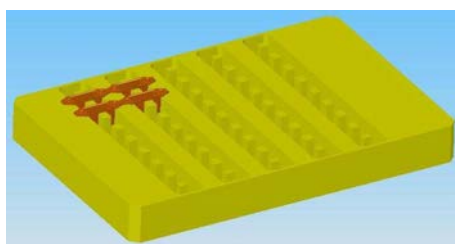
Support à cuvettes aux dimensions d'une plaque 96 puits
